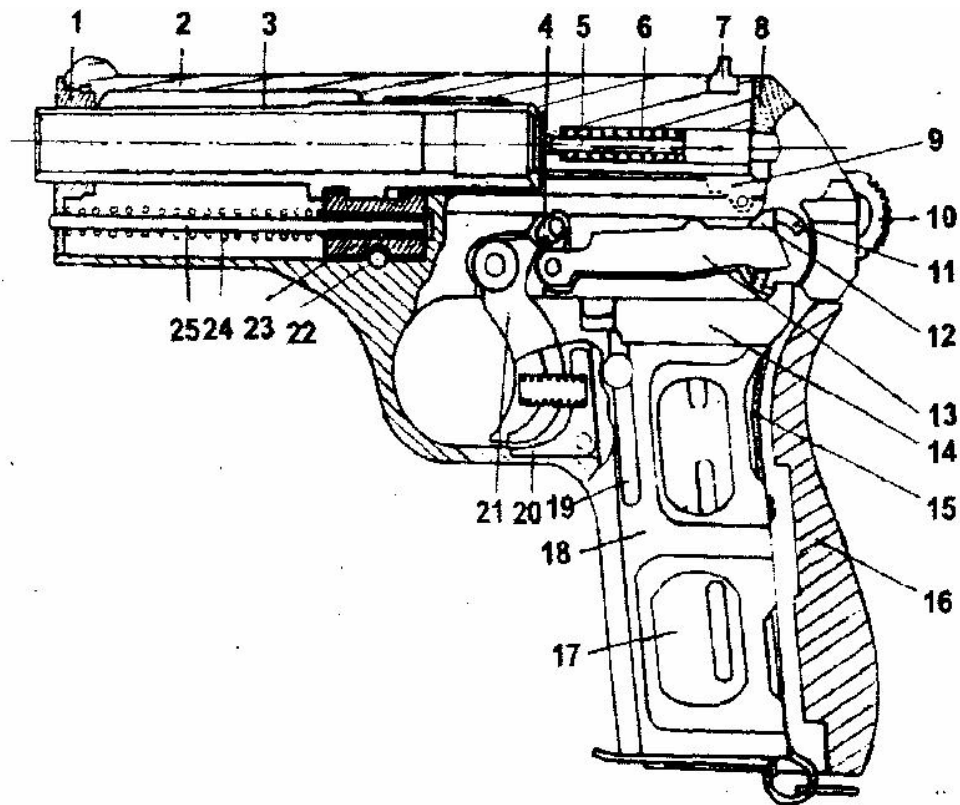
Устройство пистолета Чешска Зброевка мод. 27:
